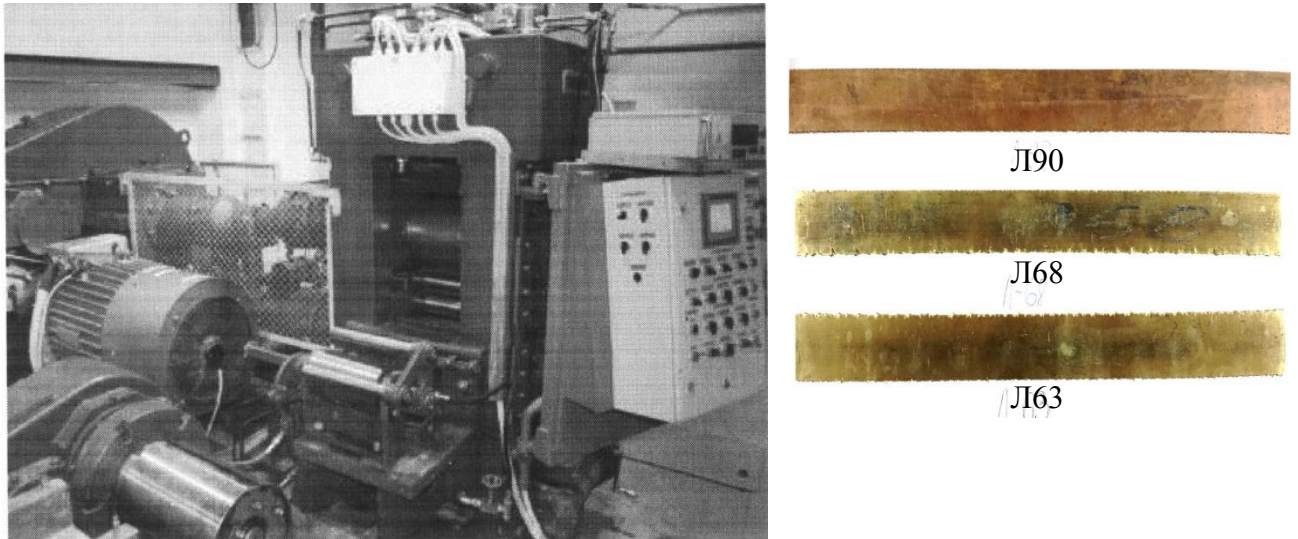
Стан 320 дуо-кварто и общий вид прокатанных образцов
